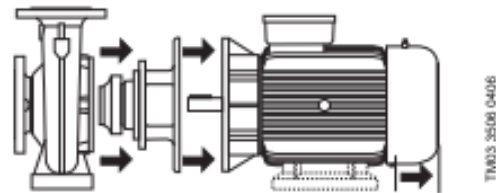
Vista esquemática del principio de desmontaje para bombas NB y NBU (NBU con patas en el motor)
